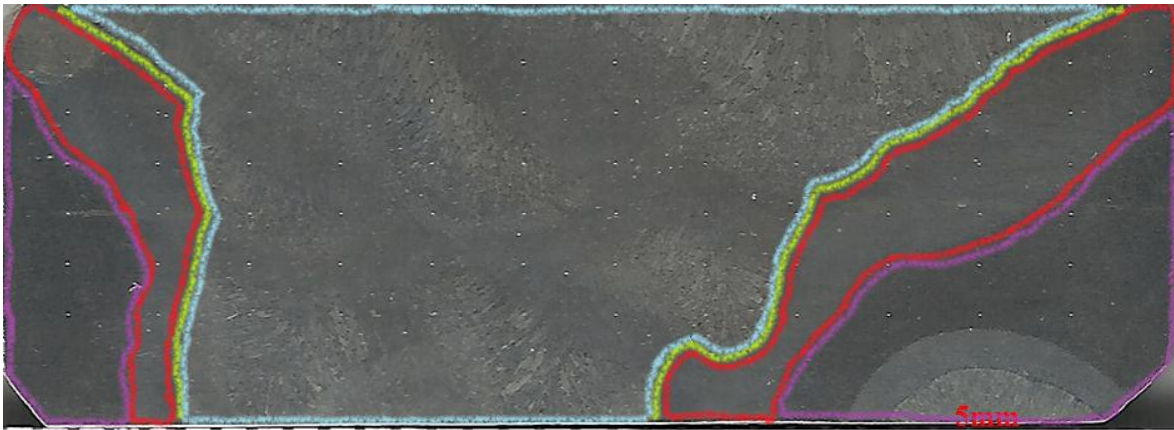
Identificación de las zonas que se presentan en soldadura.
